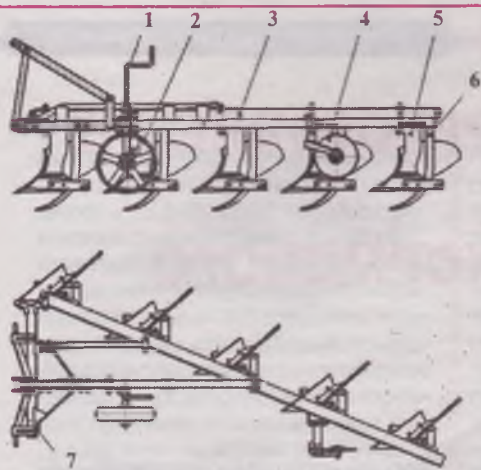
Плуг ПЛН-5-35ПМ: 1 — регулировочный винт; 2 — опорное колесо; 3 — рама; 4 — дисковый нож; 5 — корпус; 6 — рыхлительная лапа; 7 — автосцепка
